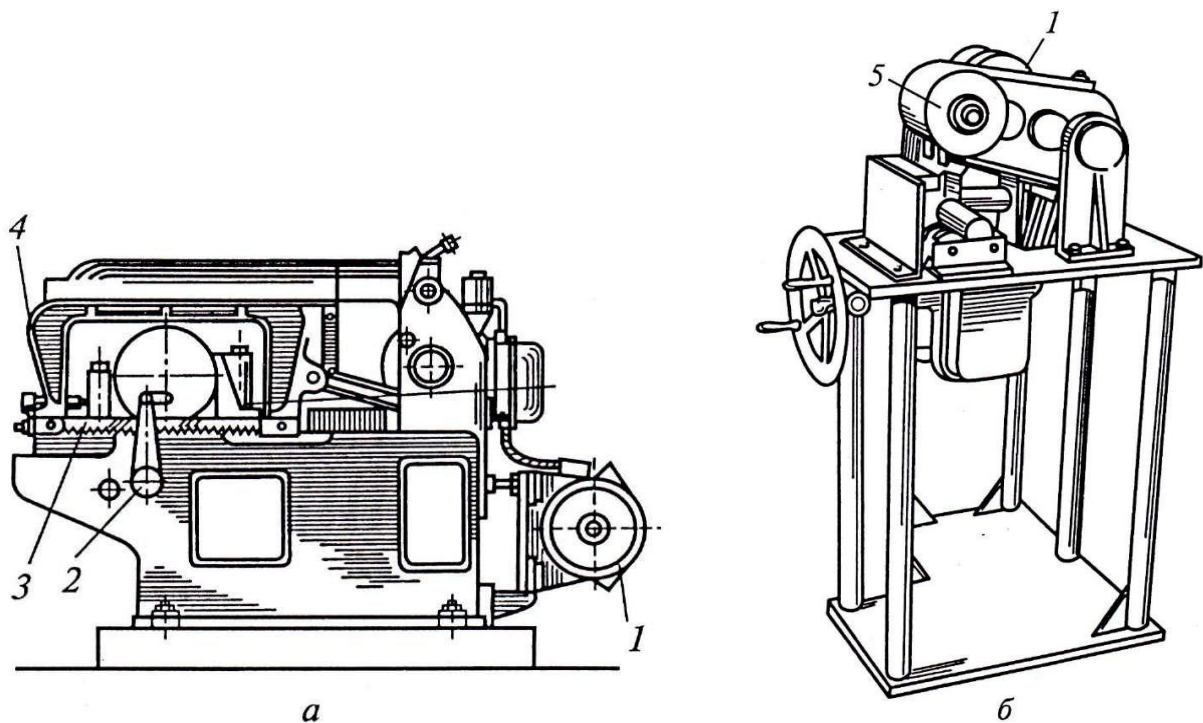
Механічне різання металу: *а* – приводний ножівковий верстат 872А, *б* – трубівідрізний механізм ВМС-32; 1 – електродвигун; 2 – упор; 3 – ножівкові полотна; 4 – пиляльна рама; 5 – ріжучий диск
